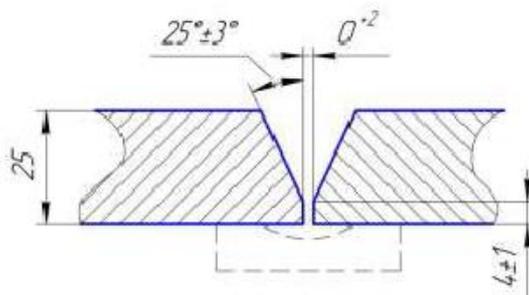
Конструктивные элементы подготовленных кромок сварного соединения
